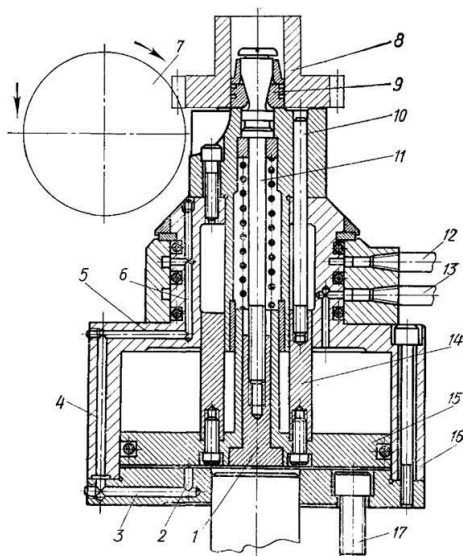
Пристосування з поршневим пневмоприводом для фрезерування зубів циліндричного колеса
